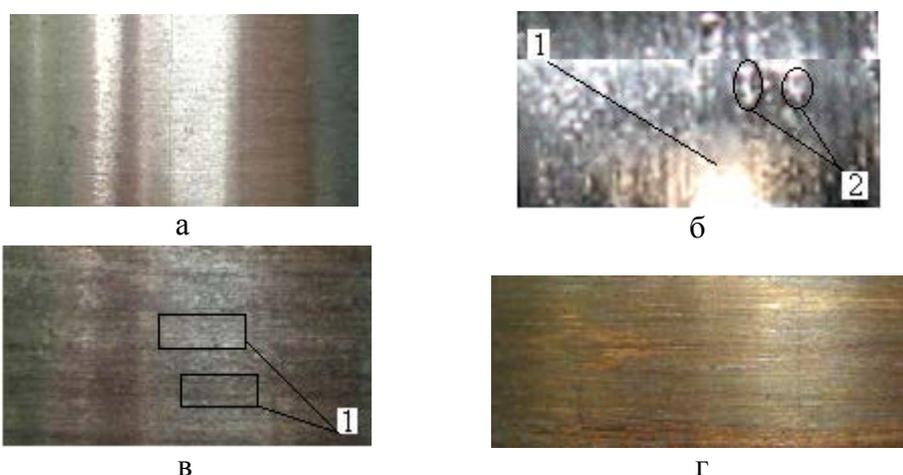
Вид поверхности образца-шейки при формировании покрытия:
